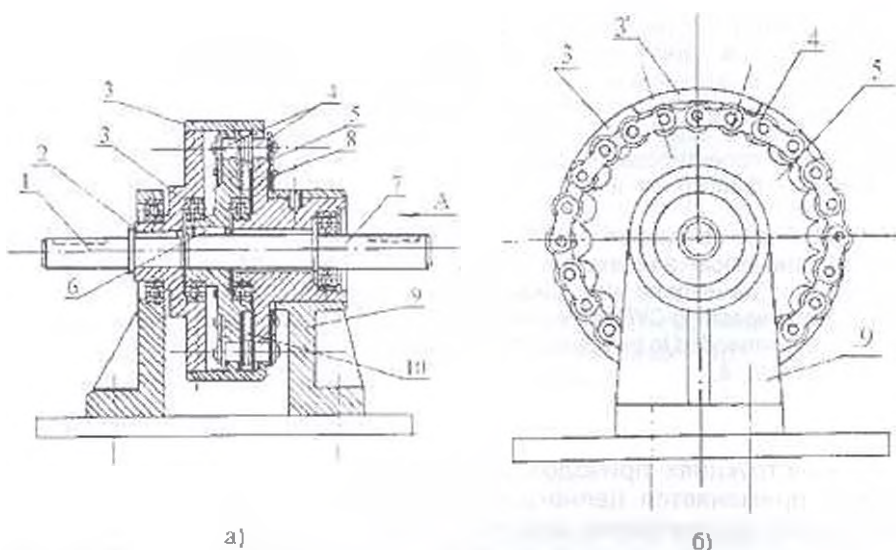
Продольный (а) и поперечный (б) разрезы общего вида конструкции двухволновой цепной передачи
